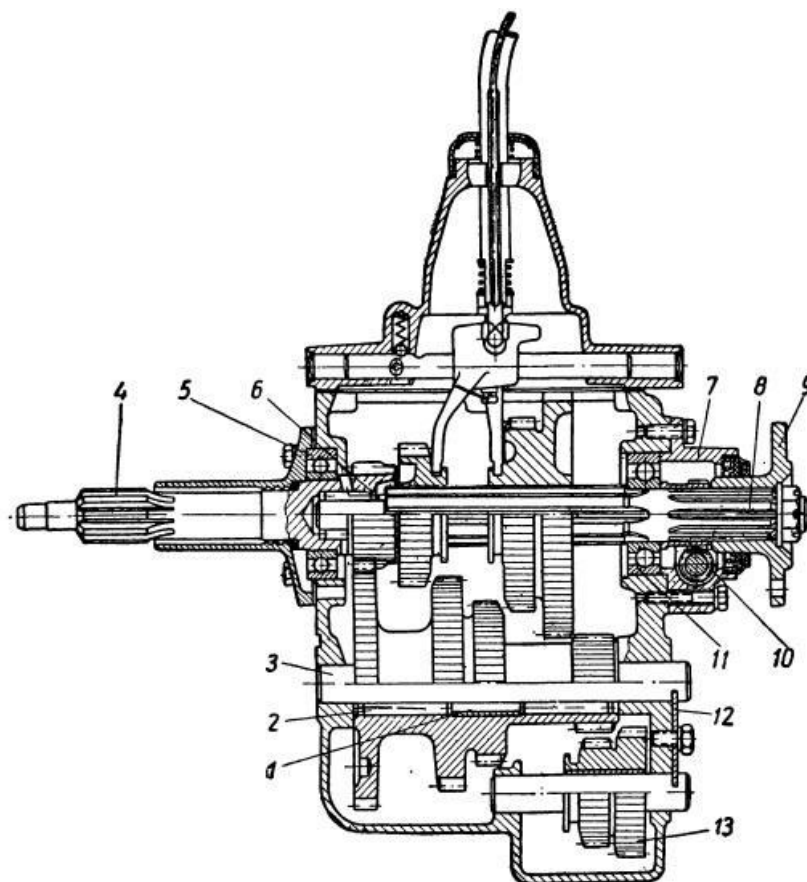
Коробка передач автомобиля ГАЗ-51:
